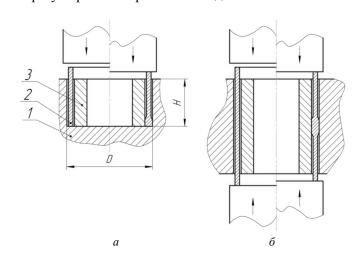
Сборка прессового соединения с промежуточной втулкой
